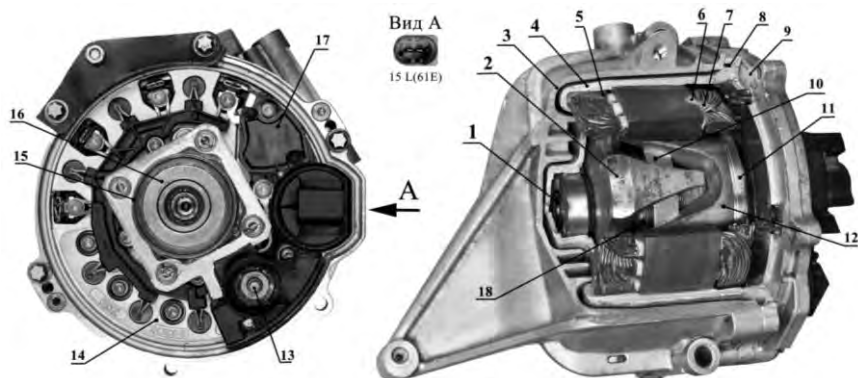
Индукторный генератор фирмы «Bosch»:
